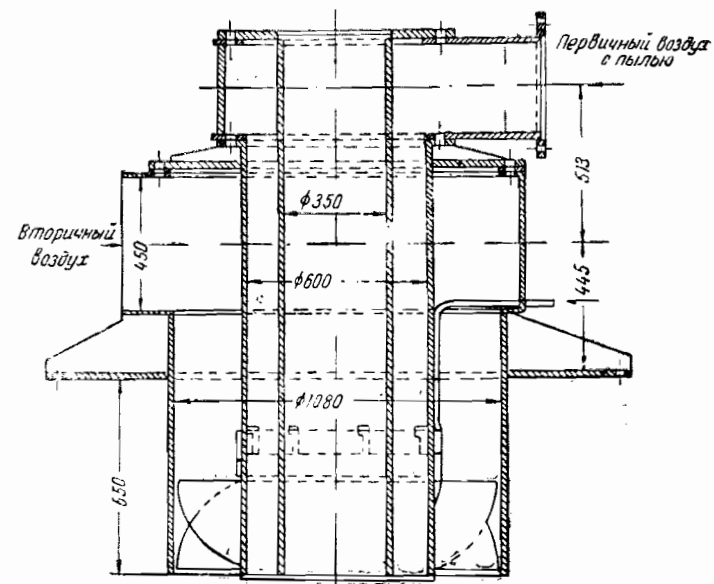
Круглая горелка ВТИ с завихрывающими поворотными лопатками
